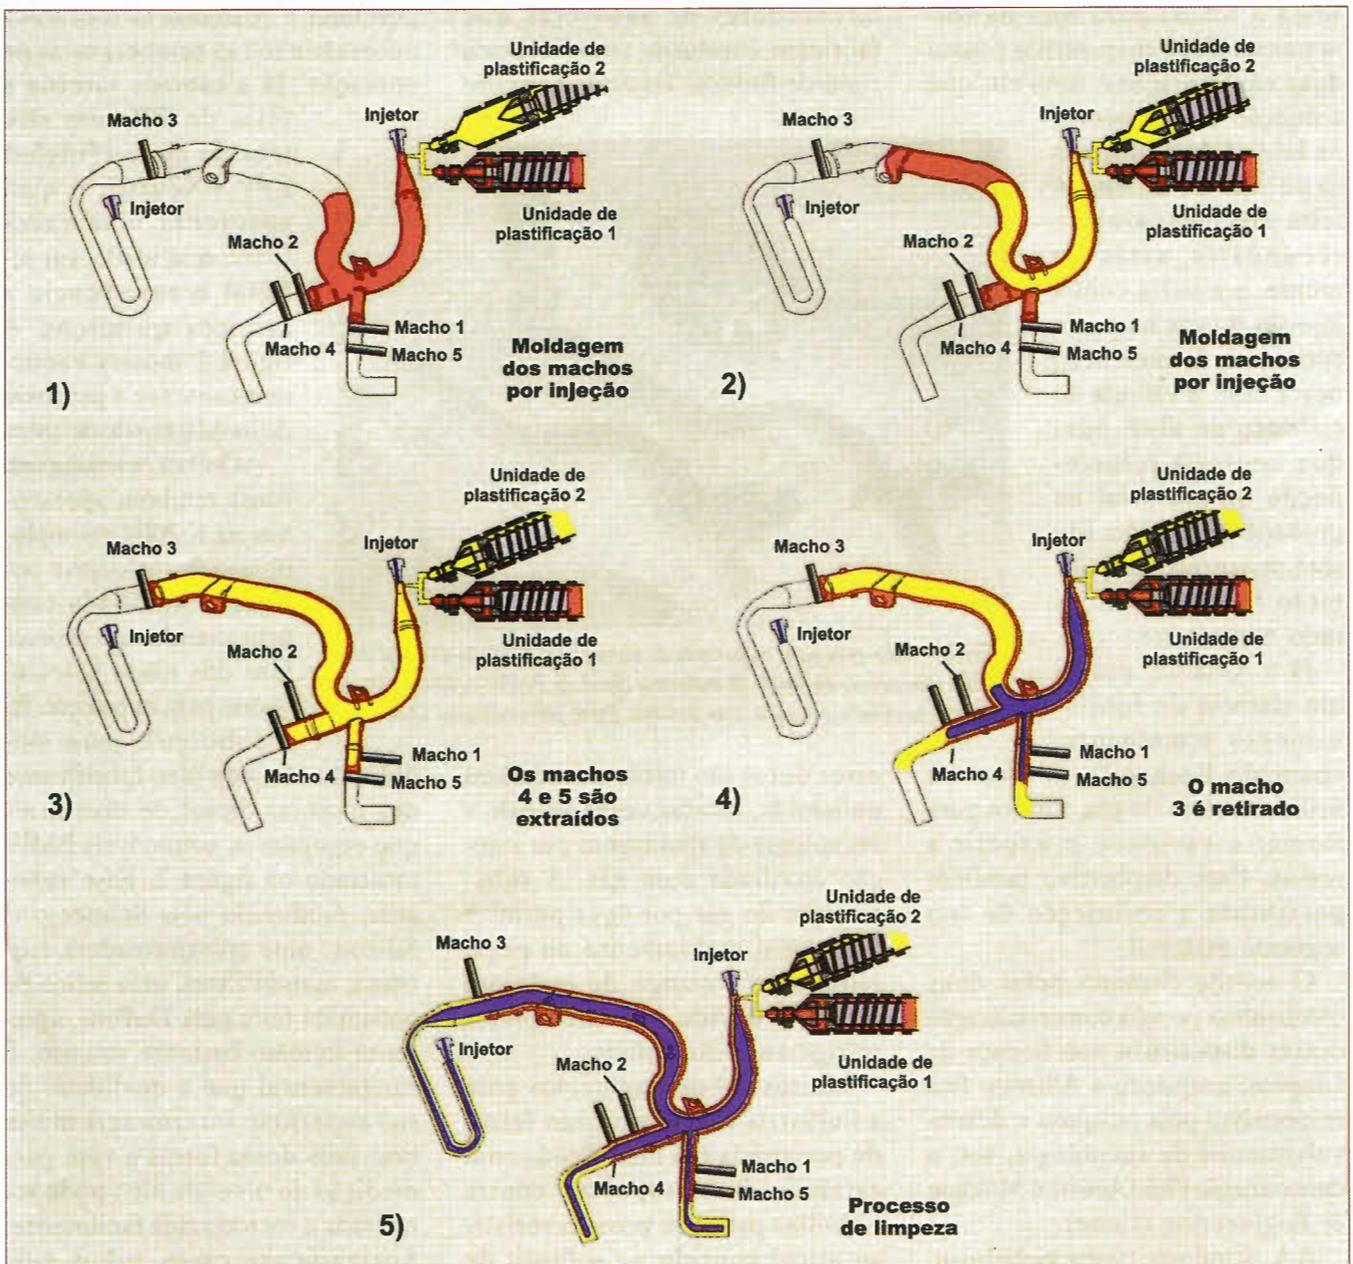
Moldagem de tubo para condução de água para arrefecimento de motores automotivos incluindo o uso de co-injeção e injeção auxiliada por água. Etapas de fabricação: 1) injeção do primeiro componente (camada externa, vermelha); 2) injeção do segundo componente (camada interna, amarela); 3) preenchimento dos ramais; 4) injeção de água; 5) circulação opcional de água e sopro com ar comprimido
